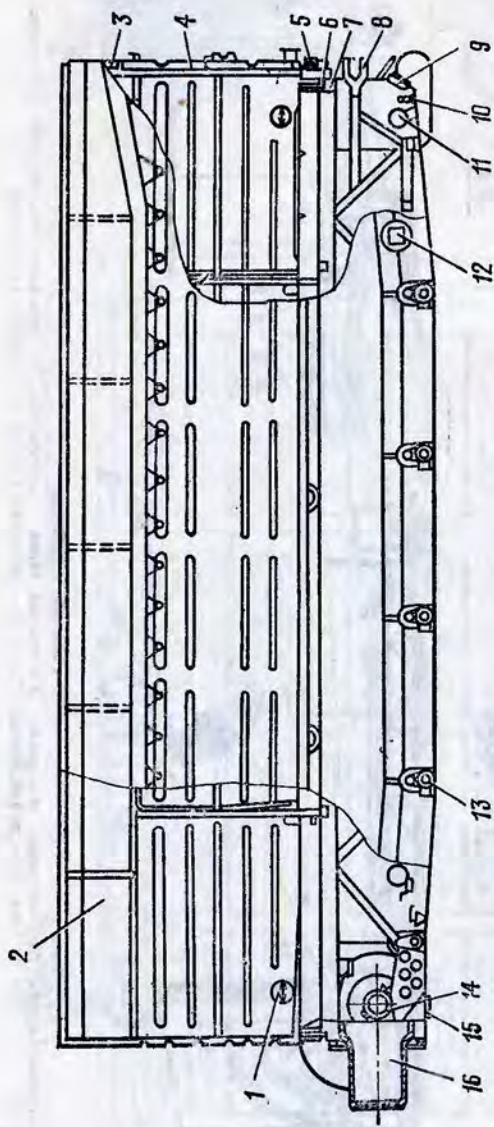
Корпус и кузов второго звена транспортера ДТ-10П:
